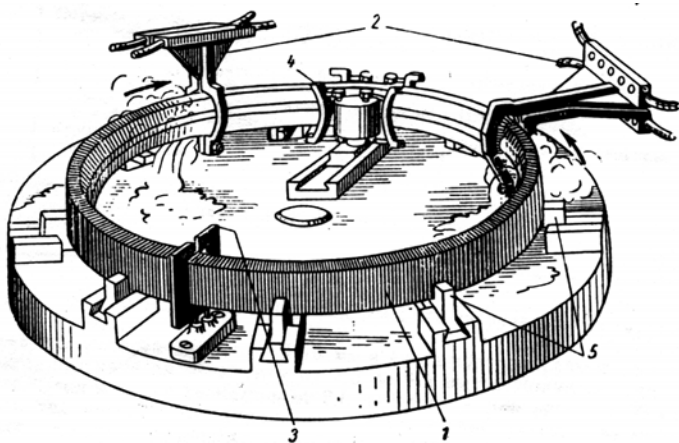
Схема пристрою для гартування парними індукторами великогабаритного кільця
